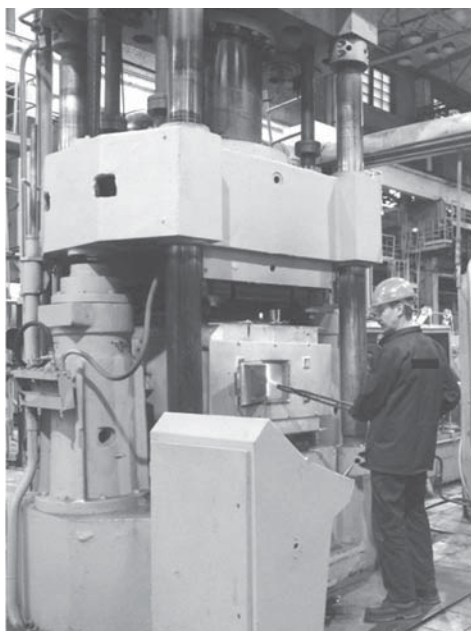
Рабочая зона пресса для изотермической штамповки
